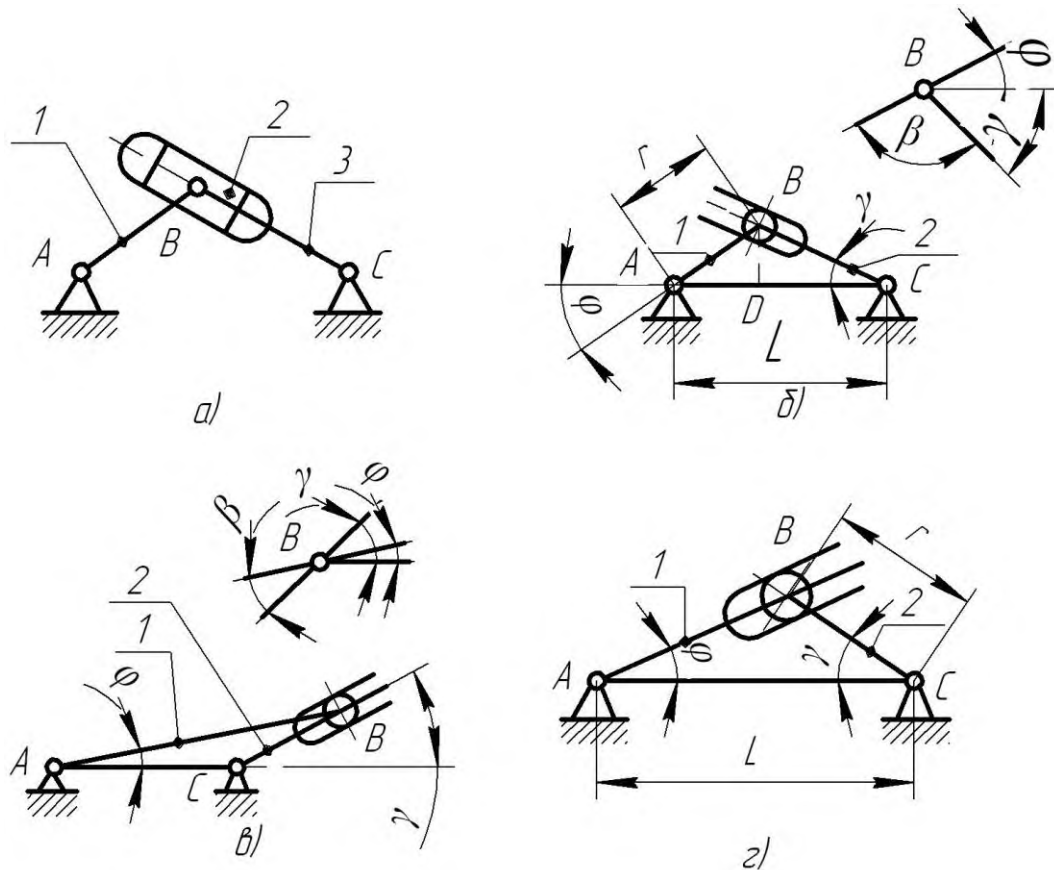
Конструктивні різновиди кулісного механізму
